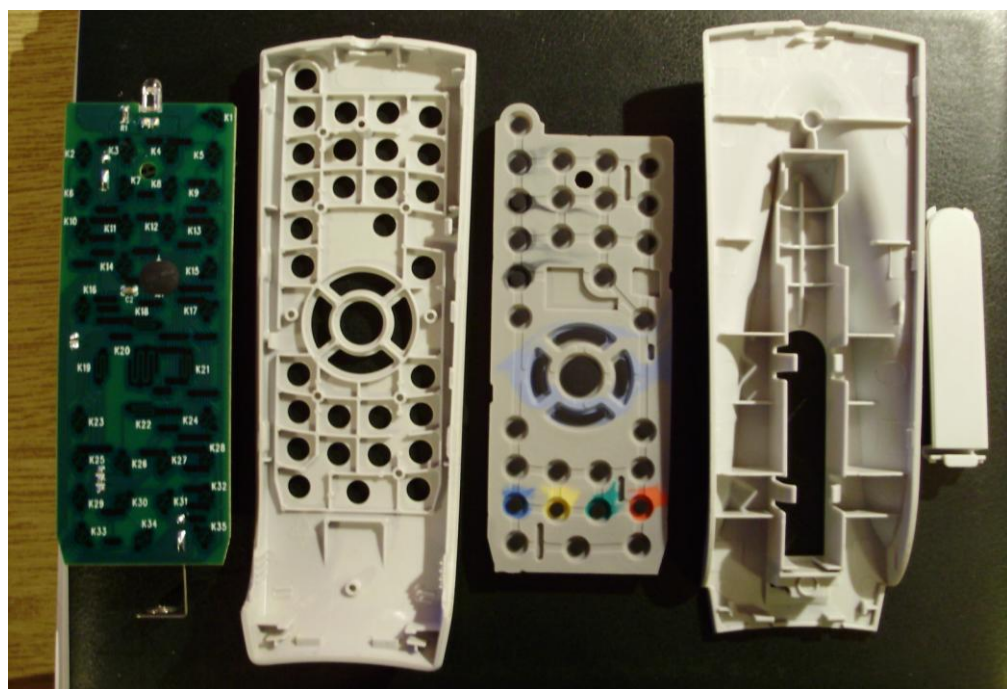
Daljinski upravljač Grundig Tele Pilot 160 C
